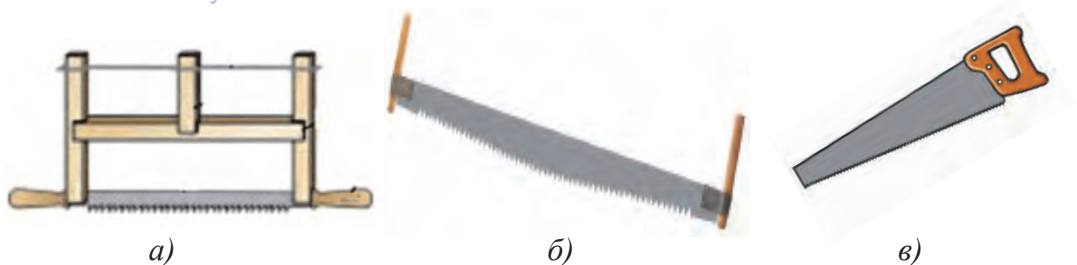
Виды пил: а – лучковая пила; б – двуручная пила; в – ножовка.
